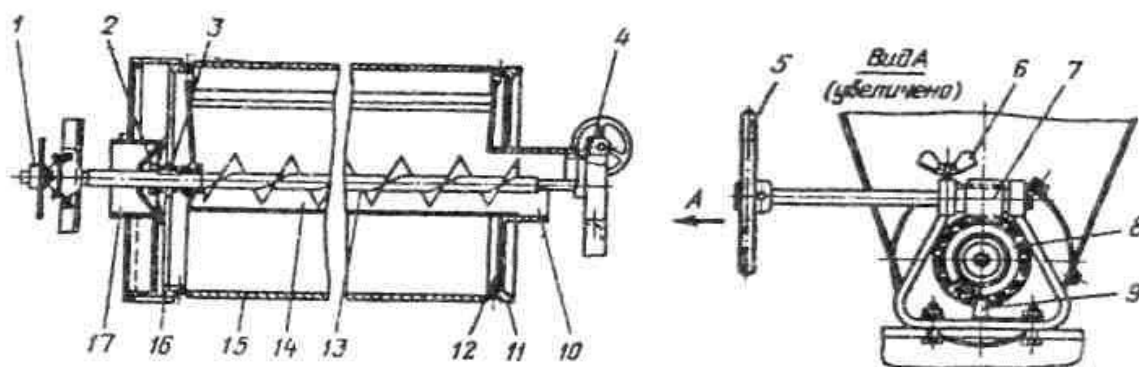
Триерный цилиндр: 1- звездочка; 2 - хомут; 3 - шпонка; 4 - кронштейн; 5 - маховик; 6 - барашек; 7— червяк; 8 - червячное колесо; 9 - стрелка указателя; 10 - горловина шнека; 11 - передняя розетка; 12 - тарельчатый круг; 13 - шнек; 14 - желоб шнека; 15 - обечайка цилиндра; 16 - задняя розетка; 17 - боковина с патрубком.
